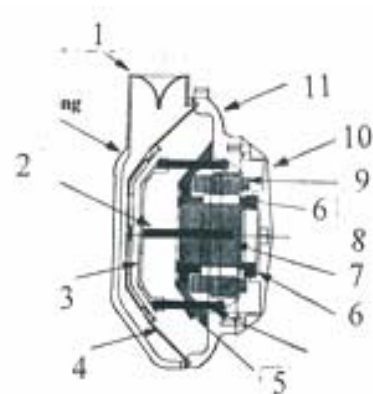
Устройство СПИ ОЛЖ Токуо TMDU VAD: 1 – НУК; 2 – винт винтовой планетарной передачи; 3 – толкатель; 4 – диафрагма; 5 – направляющие; 6 – подшипники; 7 – гайка винтовой планетарной передачи; 8 – ротор; 9 – статор; 10 – крышка; 11 – электроразъем
